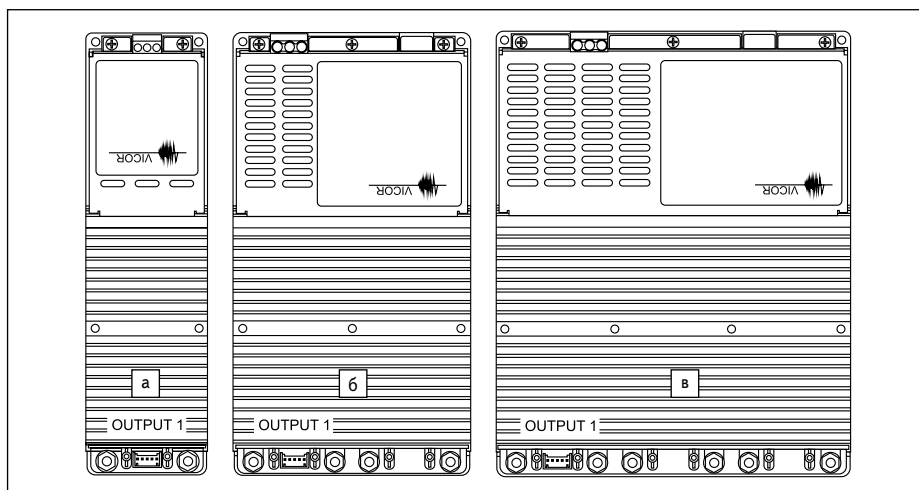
Внешний вид корпуса (вид сверху): а) 1-UP; б) 2-UP; в) 3-UP
